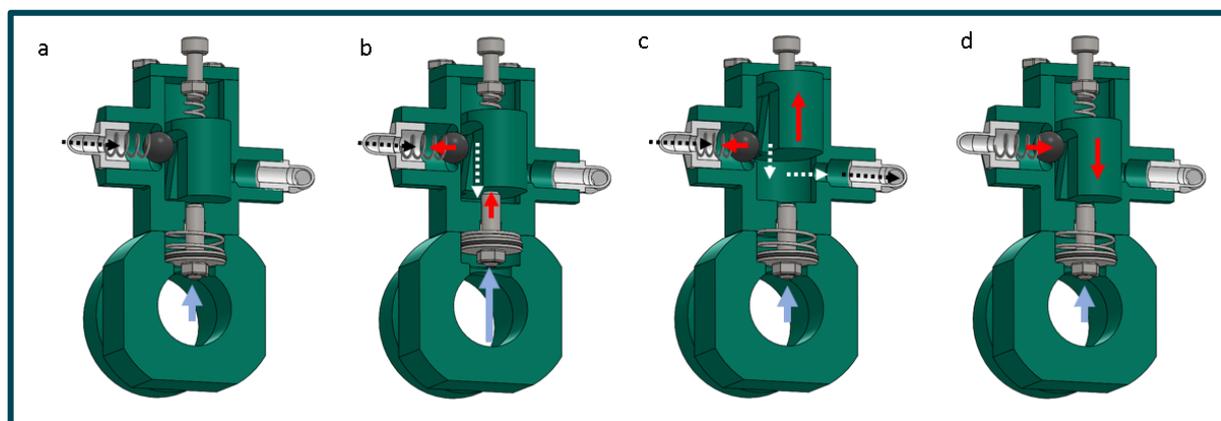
Darstellung des Initiators als Baugruppe; (a) – Initiator in Normalstellung, (b) – steigender Wasserdruck sorgt für Öffnung des Kugelventils durch den Keil-Kolben, (c) – einströmender Gasdruck hält Keil-Kolben in Selbstoffenhaltung, (d) – ausbleibender Gasdruck sorgt für Rückstellung des Initiators in Normalstellung.
